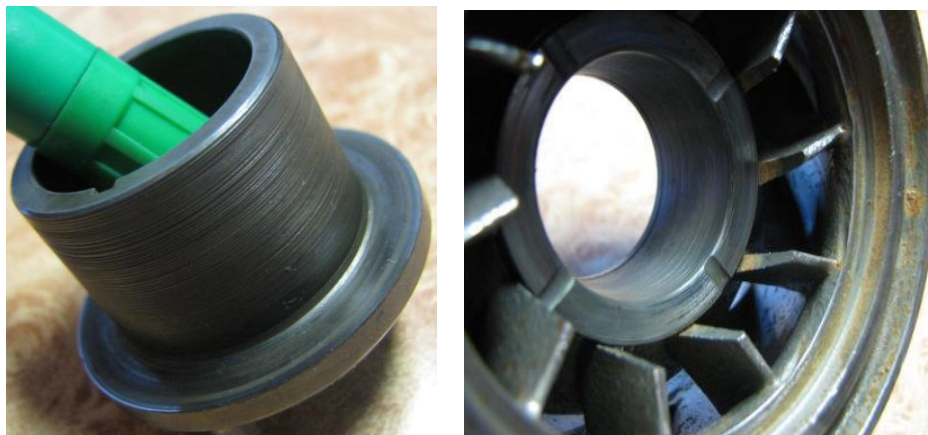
Общий вид промежуточного подшипника из твердого сплава после опыта
